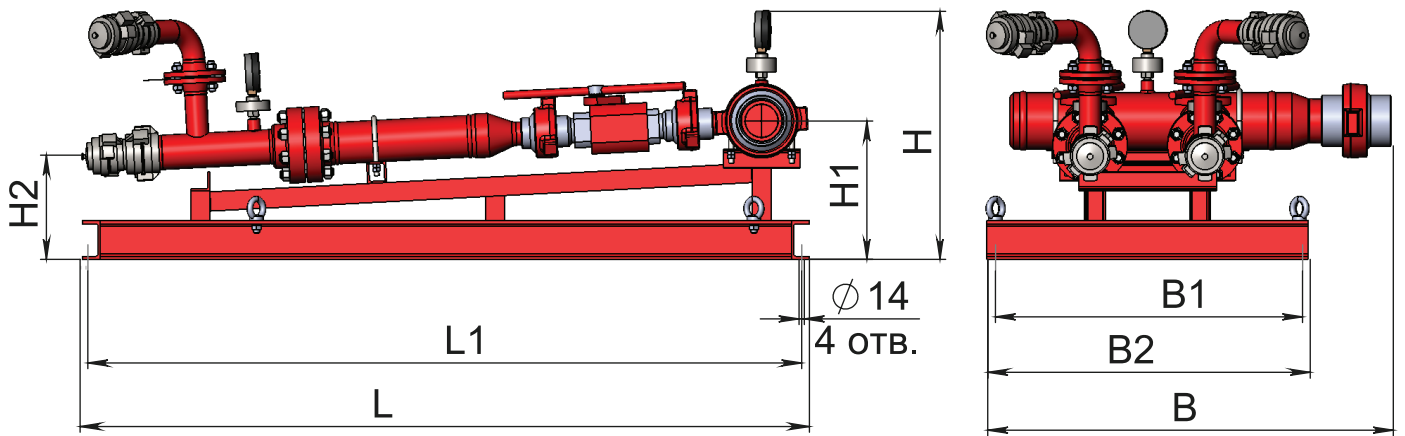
Габаритные и присоединительные размеры Бруствер-В (встраиваемое исполнение)
